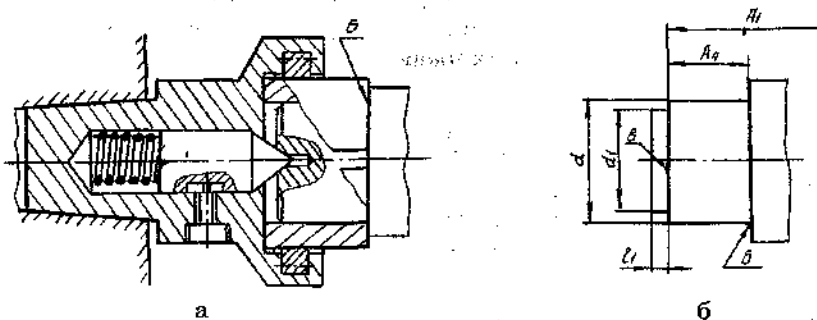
Особенности установки заготовок на токарных горизонтальных полуавтоматах: а) передний плавающий центр; б) технологическая заточка
